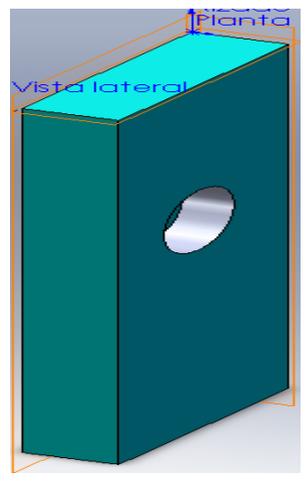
Vistas de la placa izquierda sujetadora de los rodillos tensores frontales.
